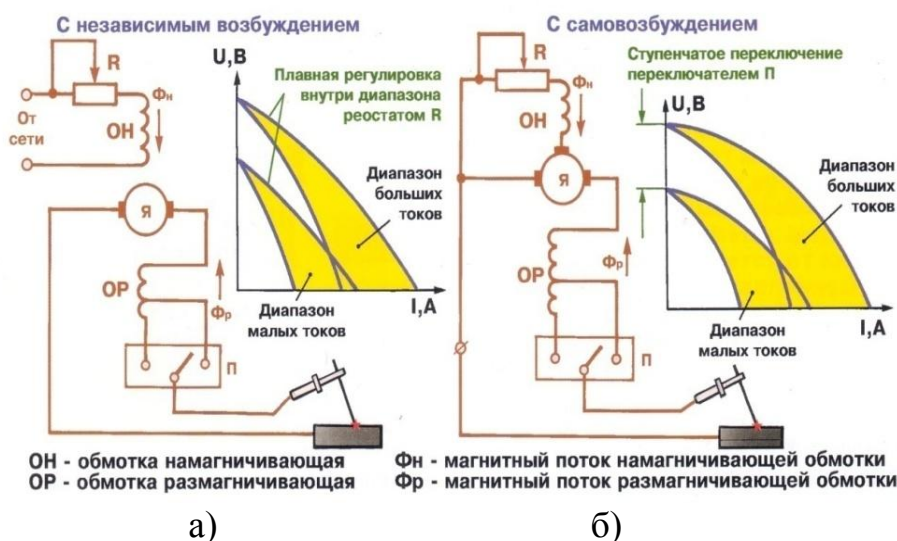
Принципиальная схема сварочного генератора:
